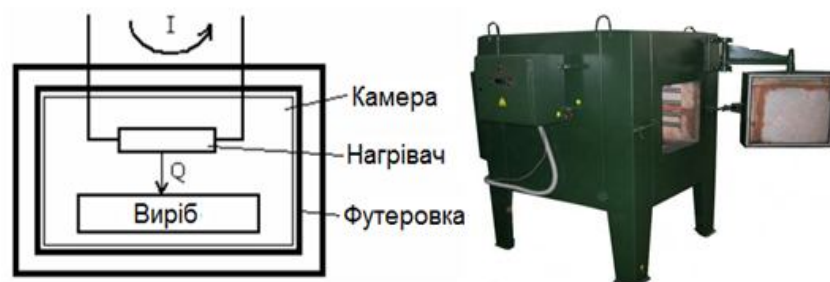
Будова електропечі опору з нагрівальними елементами
